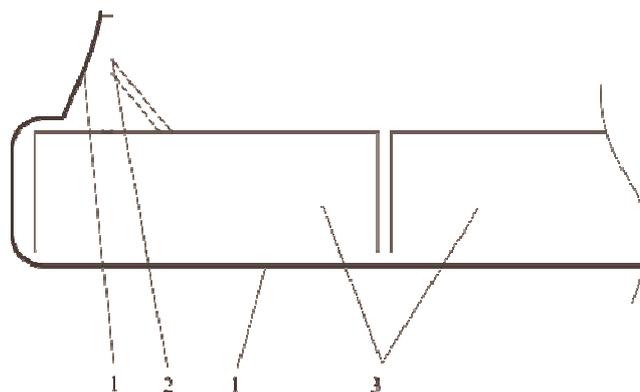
Альтернативный тип обшивки корпуса гидродинамического обтекателя: 1 – первый слой брезента, 2 – второй слой брезента, 3 – заклепка, 4 – защитный щиток.
